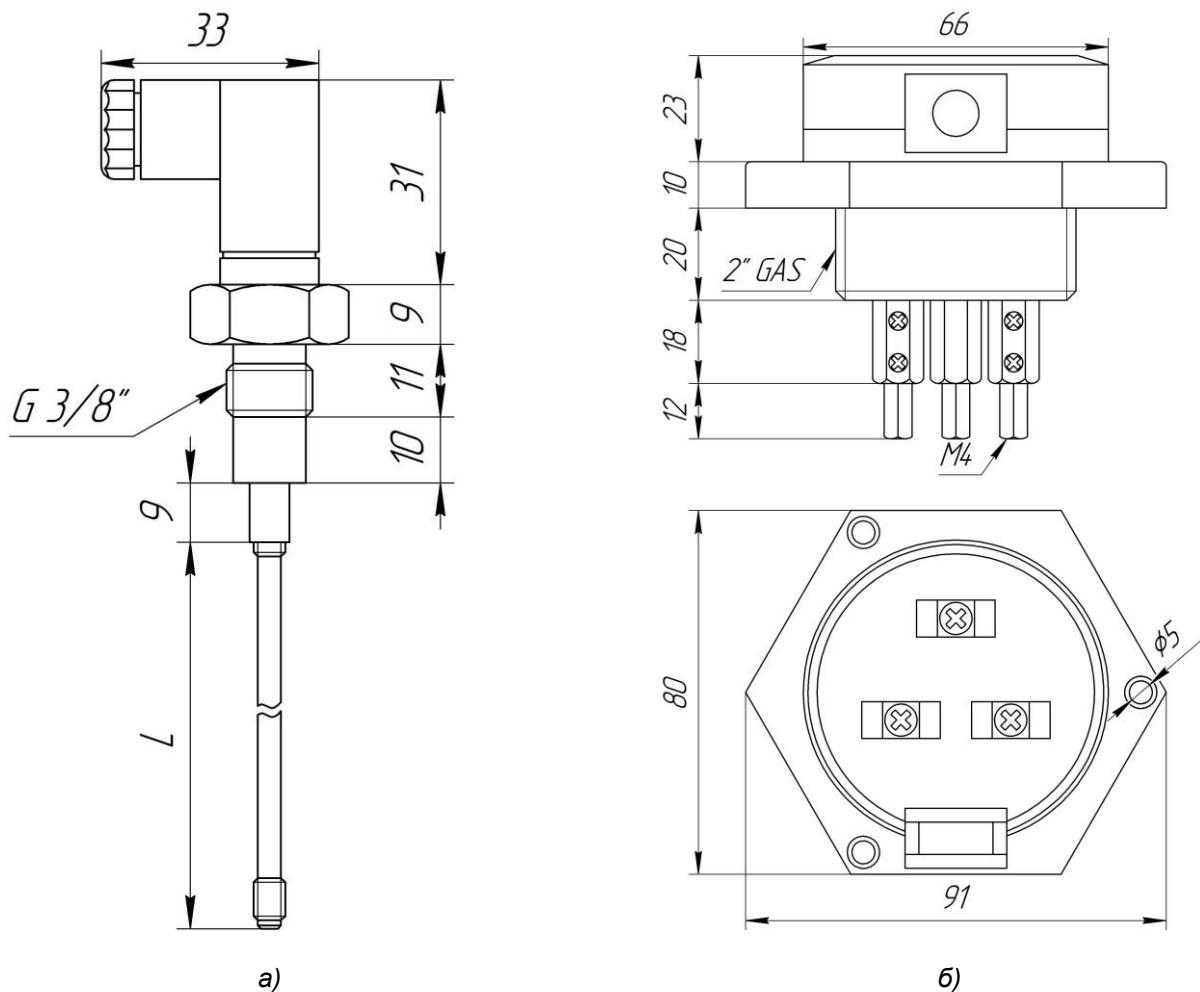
Внешний вид и габаритные чертежи датчиков кондуктометрических:
